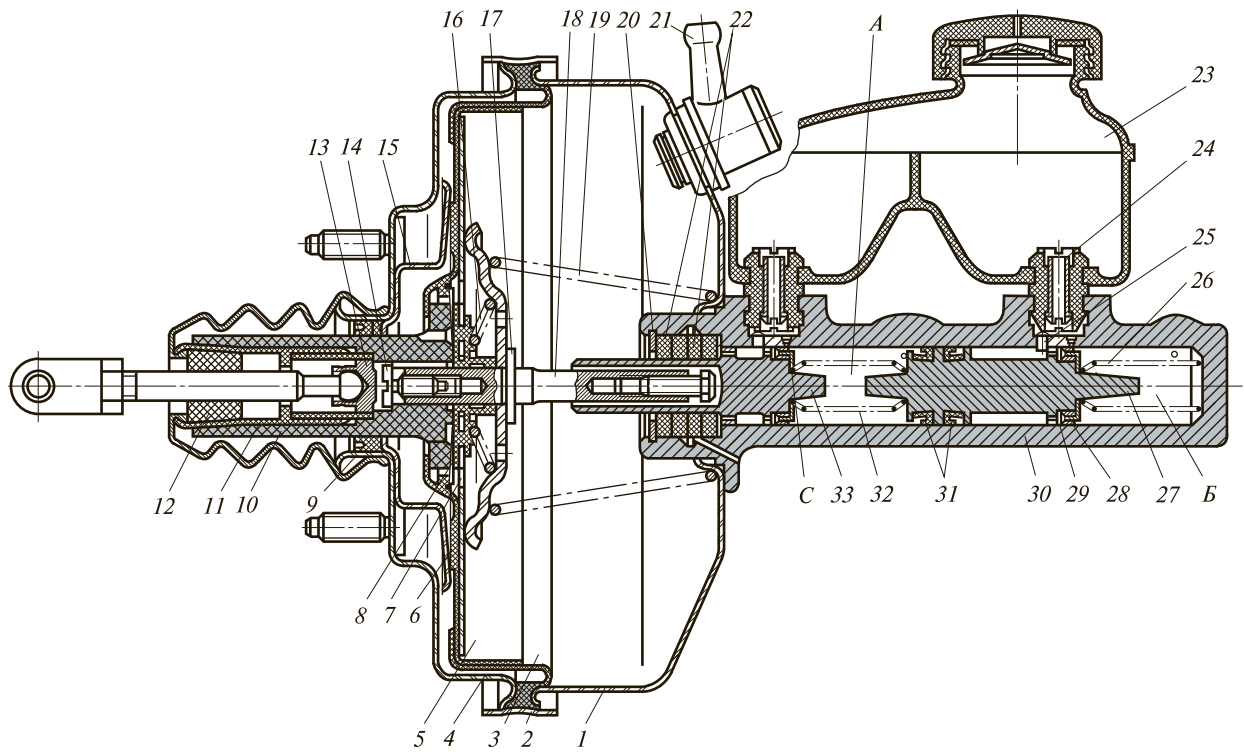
Главный цилиндр тормоза с вакуумным усилителем:
